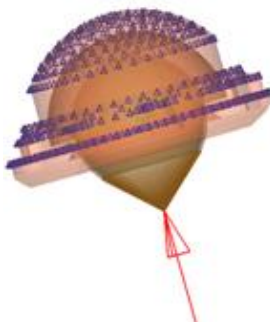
Aplicação das condições de carregamento e restrição de movimento.
